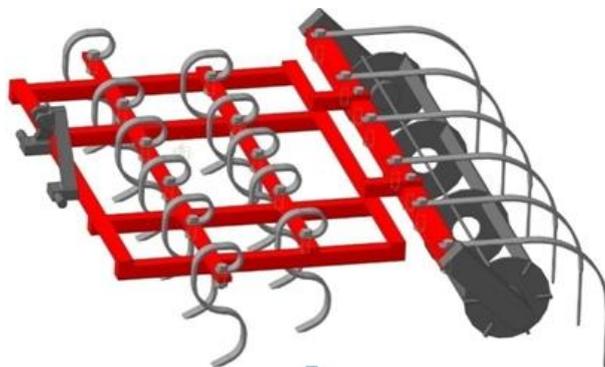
3D модель малогабаритного почвообрабатывающего агрегата
